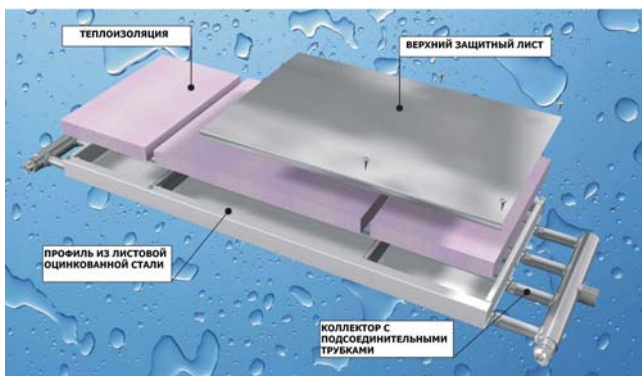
Закрывающая пластина на сварных соединениях с варьируемой длиной.
